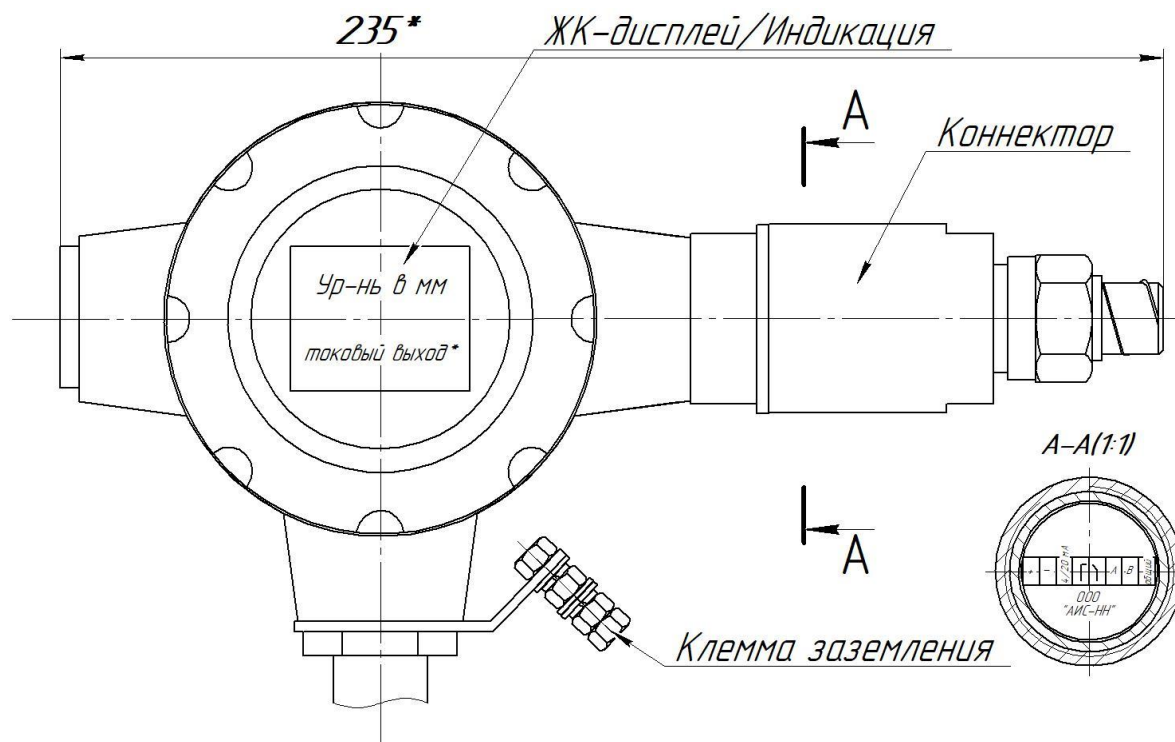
Корпус из нержавеющей стали (IP65/IP67).
